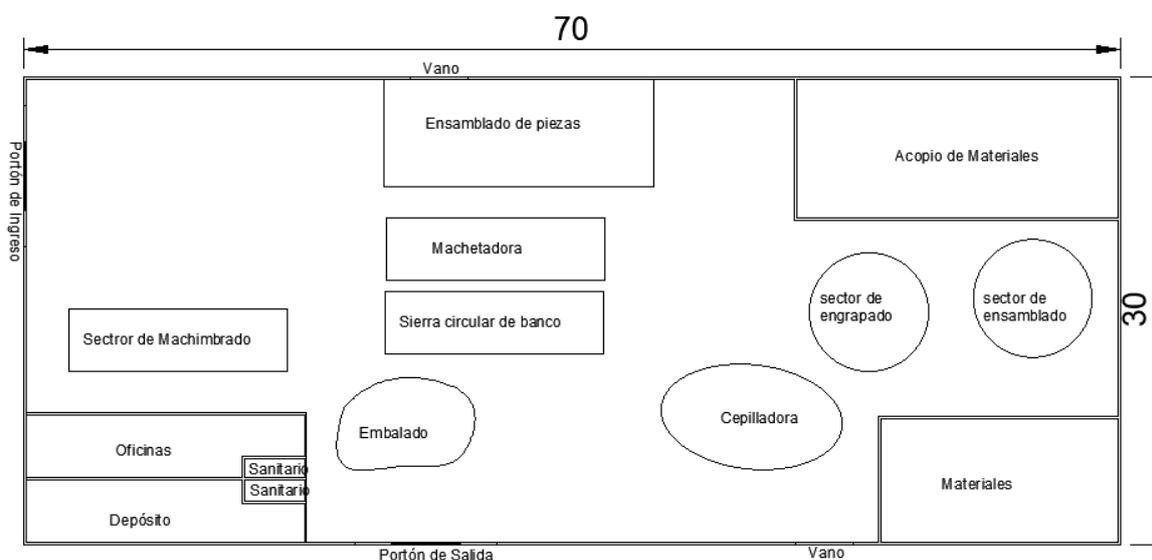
LAYOUT DE LA CARPINTERÍA.
